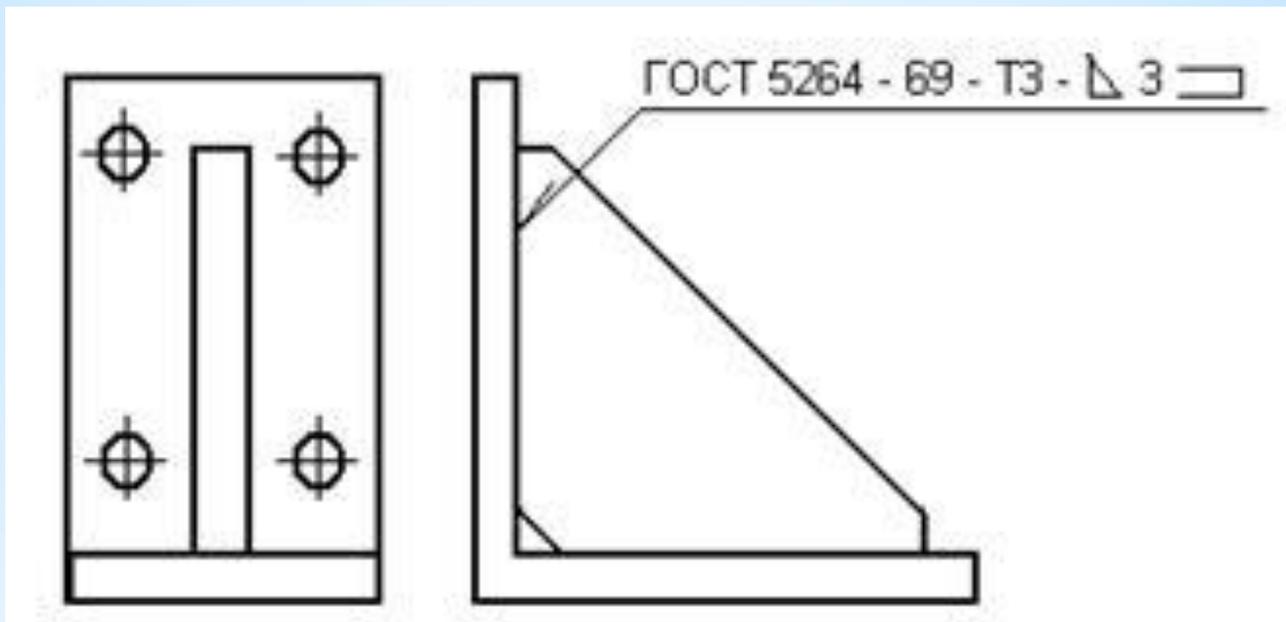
Структура условного обозначения сварного шва:
